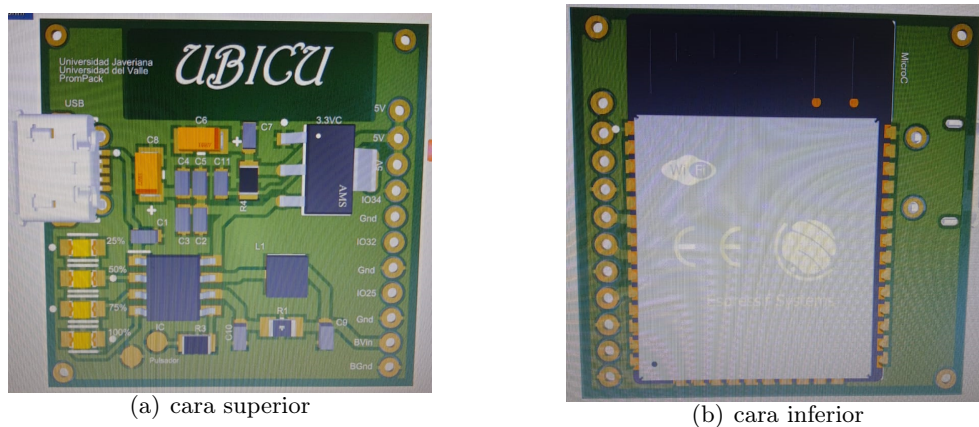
CAD PCB primer prototipo del dispositivo Ubicu.
